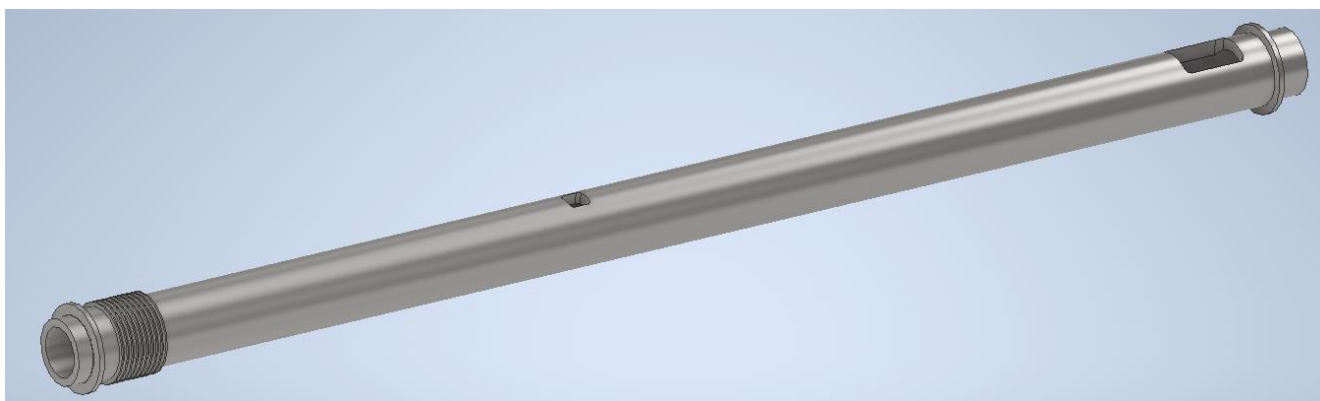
Загальний вигляд 3-Д моделі циліндричної частини корпусу.
